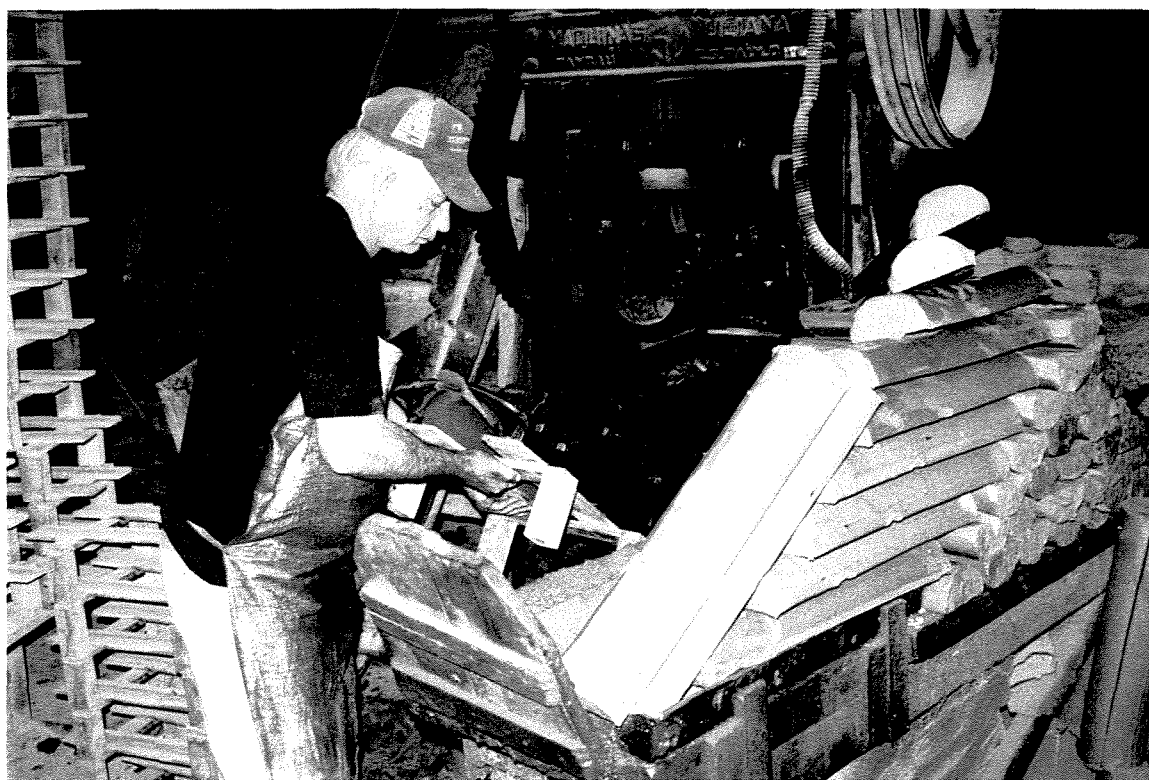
e 24 - Etapa de extrusão (lastra) e de moldagem (prensa)
